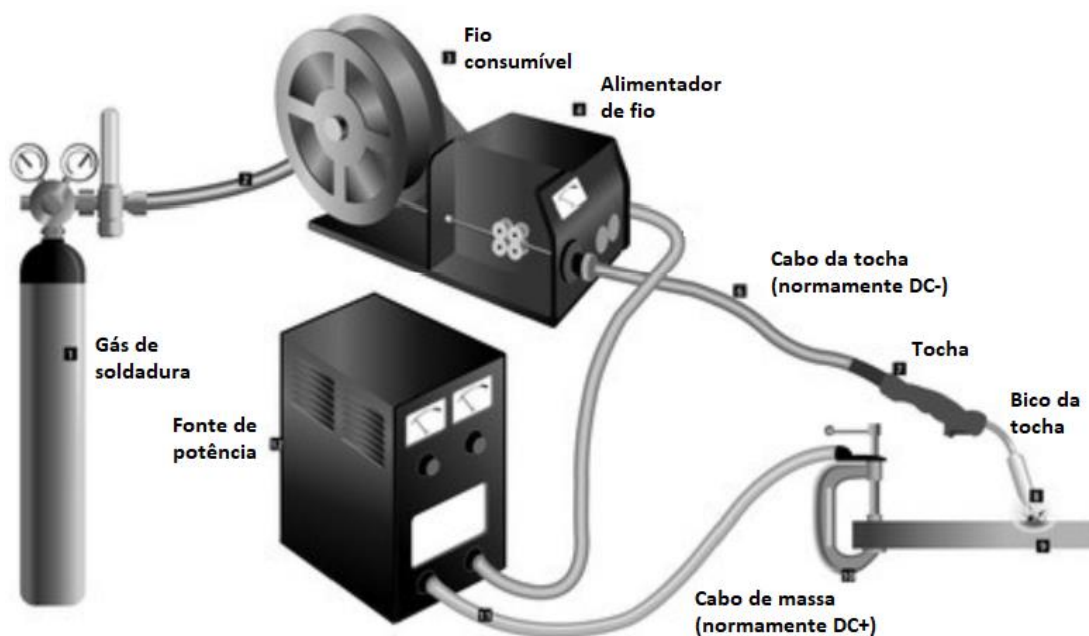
Equipamento de soldadura MIG/MAG [16]
